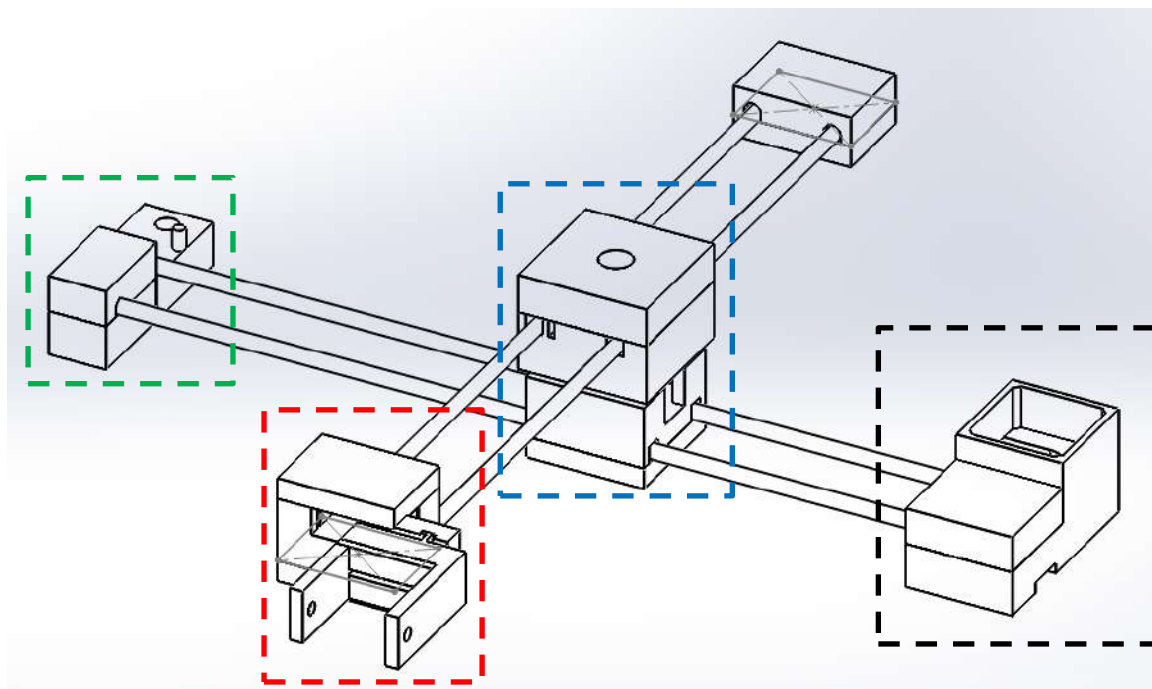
Ізометричний вигляд конструкції верстата
